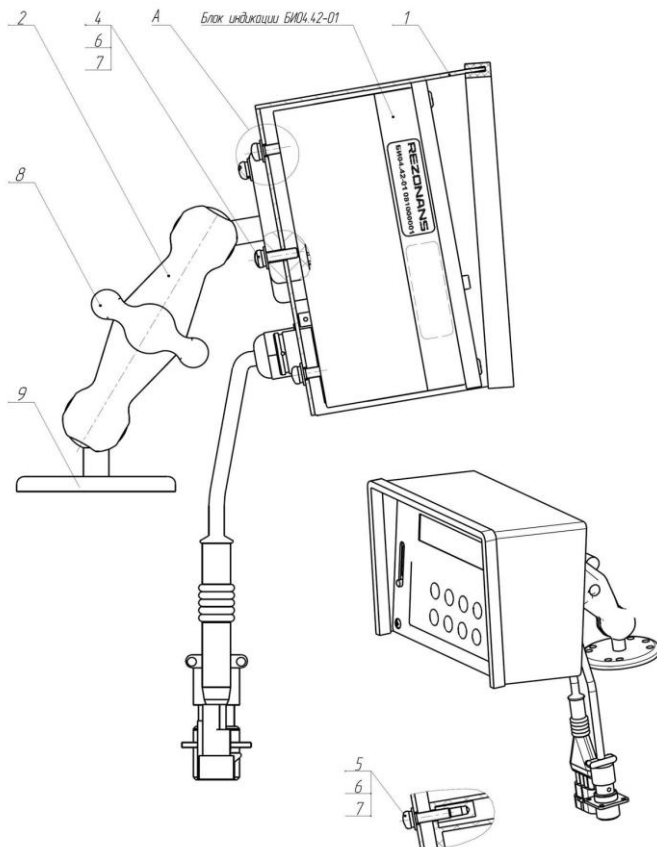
Габаритные и присоединительные размеры блока индикации БИ04.42
